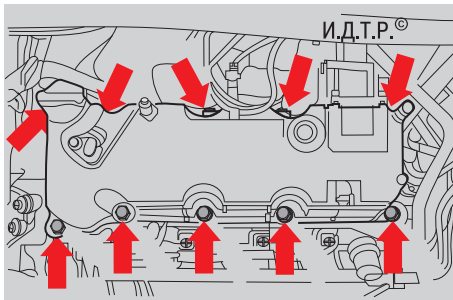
Болты крепления крышки головки блока цилиндров
